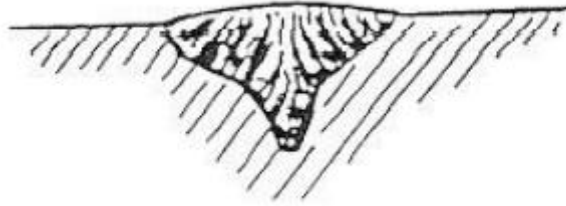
Aspecto de cordón de soldadura usando Argón
